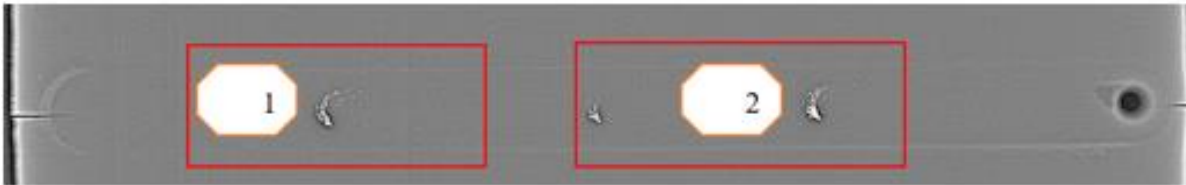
Radiografía soldadura por fricción agitación de Aluminio por la técnica digital.
